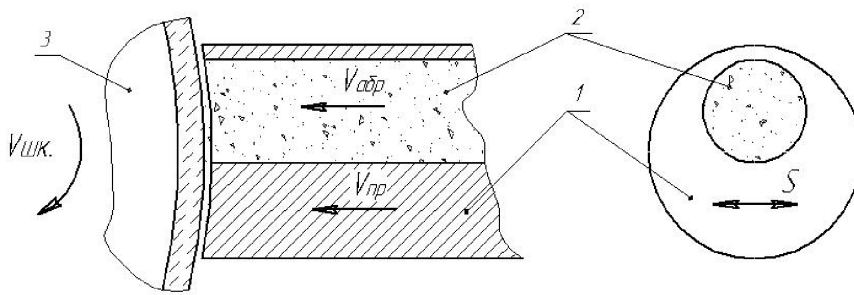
Схема процесса правки шлифовальных кругов свободным абразивом:
